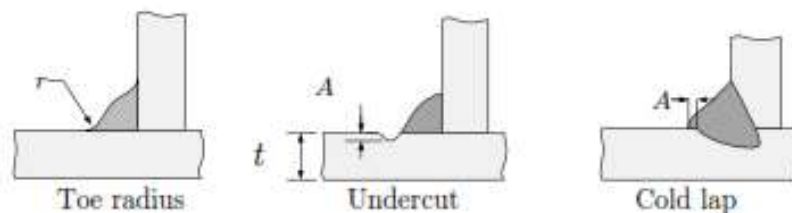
Exemples de défauts/imperfections de soudure.
